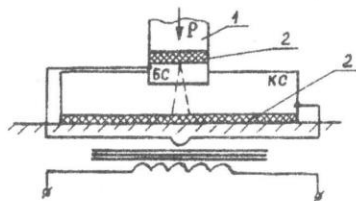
Схема сварки БС и КС для изготовления резцов: 1 – сила пресса; 2 – асбестовая прокладка
